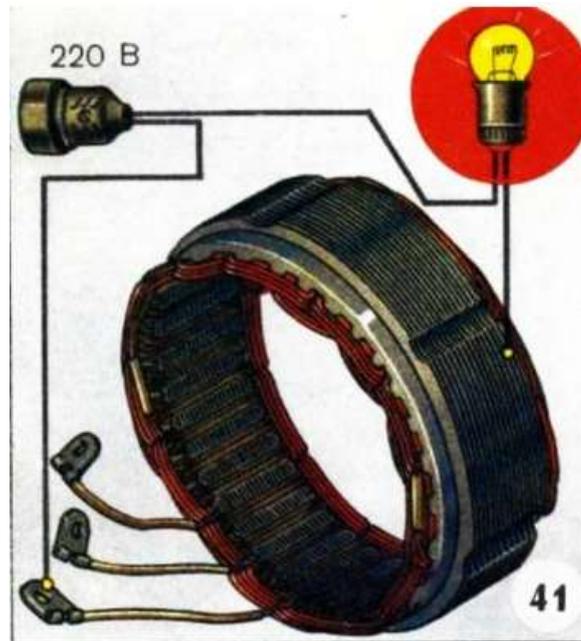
Проверка обмотки статора на замыкание с корпусом
